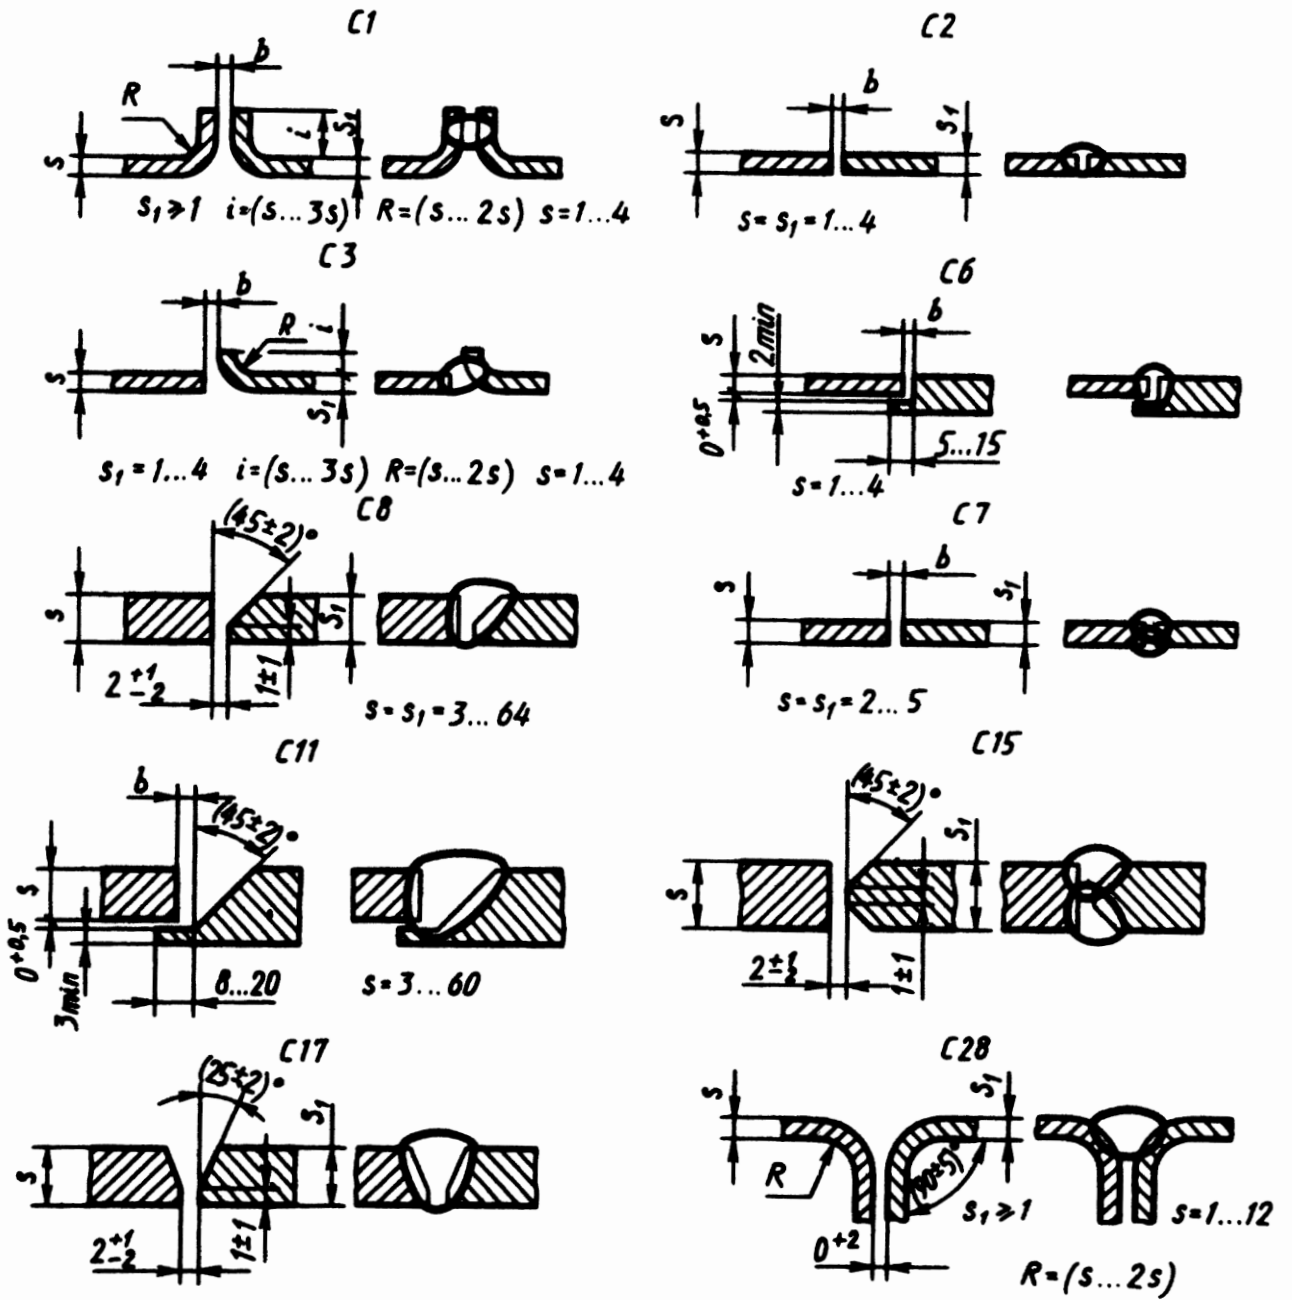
Форма поперечного сечения подготовленных кромок с размерами и сварного шва, а также стандартные условные обозначения стыковых - C1...C17 сварных соединений.
